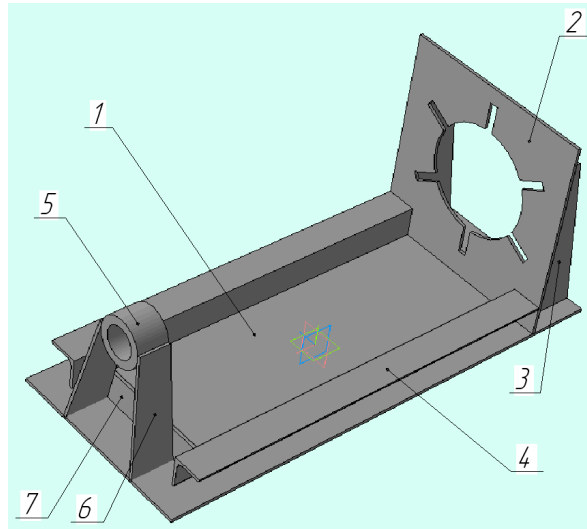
Приспособление для разборки, сборки поршня с передней крышкой тормозного цилиндра
